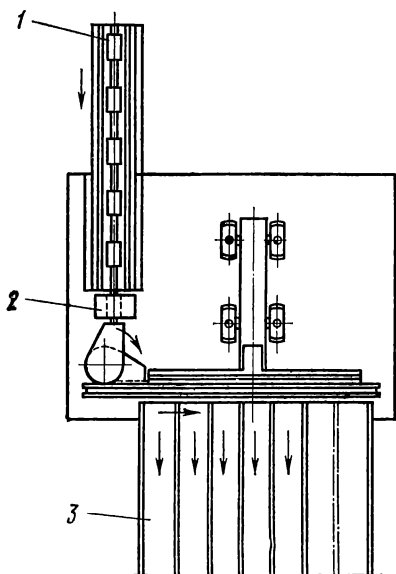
Схема универсального контрольного автомата для сортировки пальцев разных размеров
